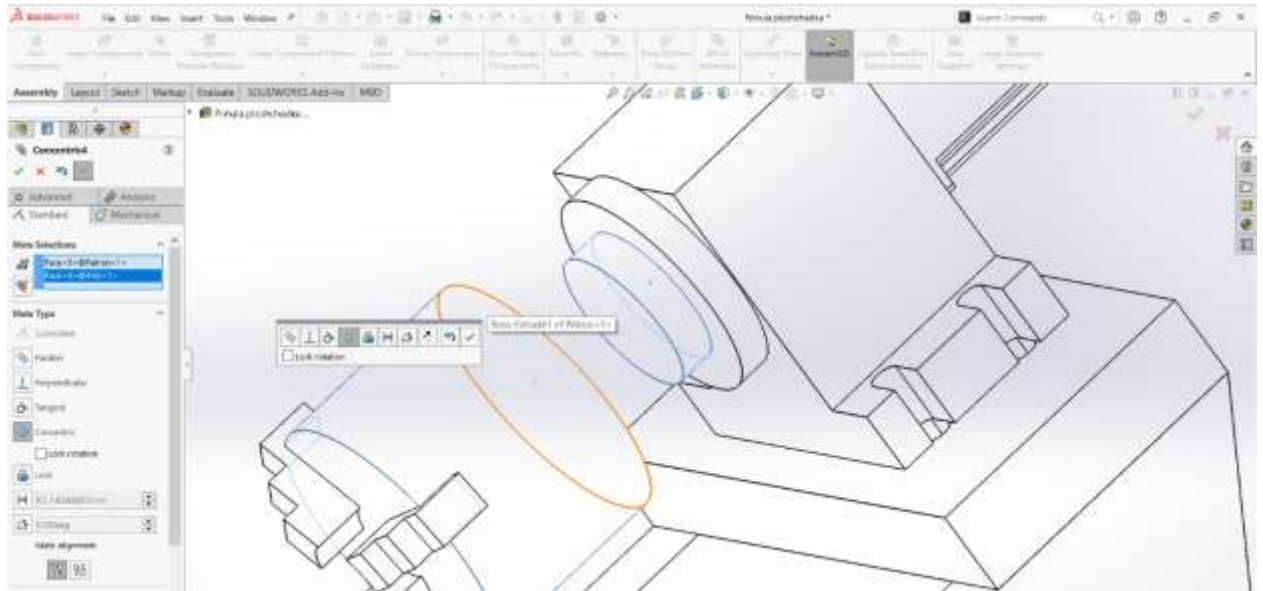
Розташування циліндричних поверхонь концентрично
